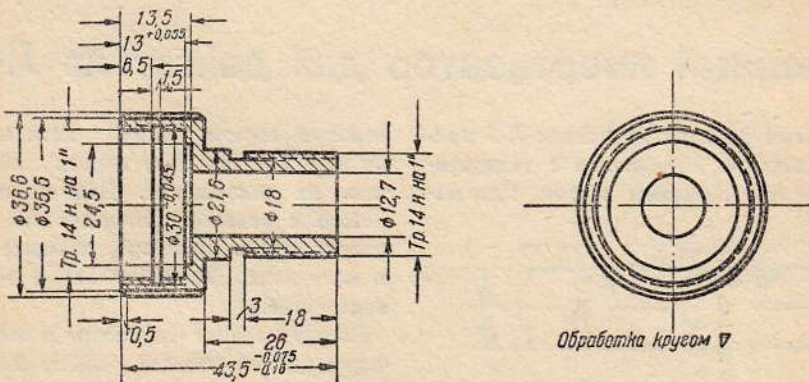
Втулка для шарикоподшипника стабилизатора скорости (со стороны гладкого барабана)
